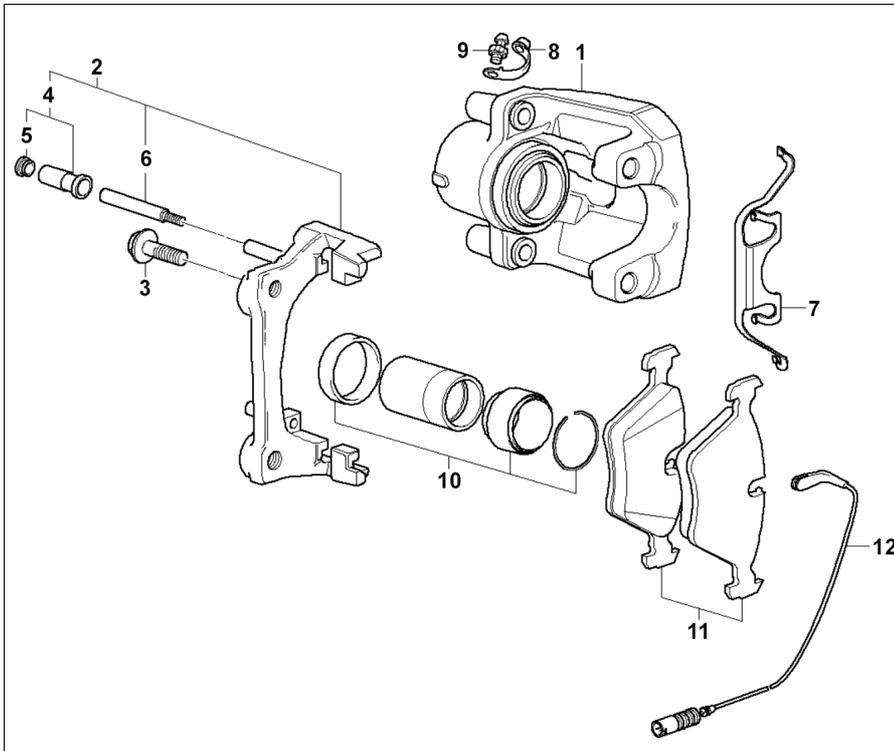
Тормозной механизм задних колес. 1 - корпус суппорта, 2 - направляющая тормозных колодок, 3 - болт (M10x26,5), 4 - направляющая втулка, 5 - пробка, 6 - направляющий палец, 7 - фиксирующая пружина, 8 - пылезащитный колпачок, 9 - штуцер прокачки, 10 - уплотнители, 11 - тормозные колодки, 12 - датчик износа.
